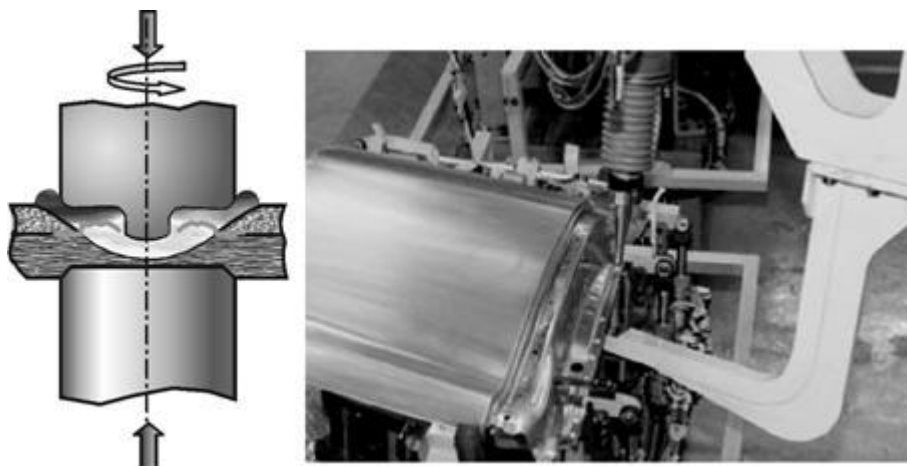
Схема точечной сварки трением, используемая фирмой MAZDA, и устройство для ее выполнения.
